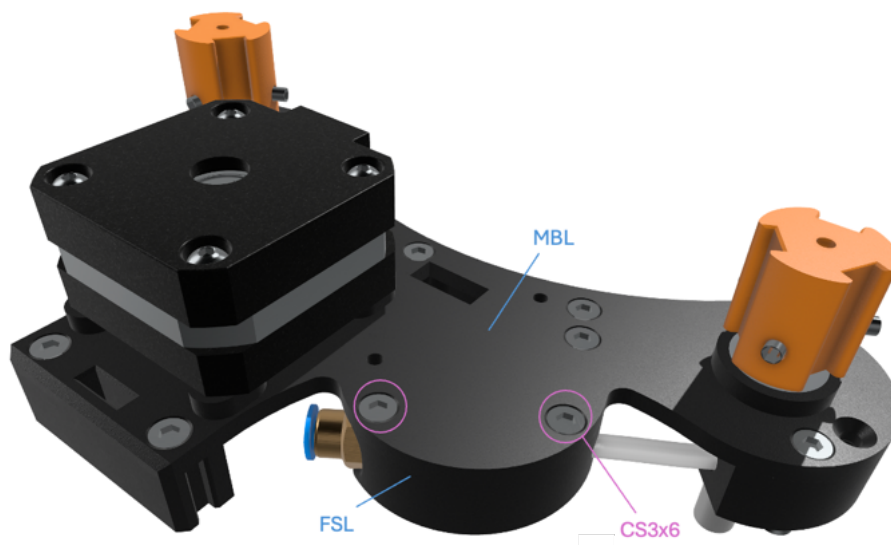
Rewinder-Chassis Montageschritt 20.
